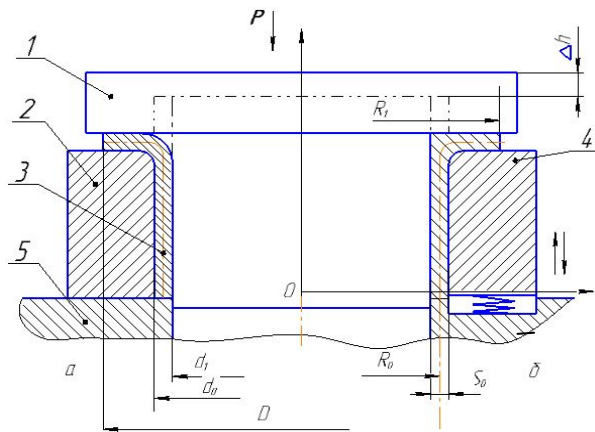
Схема раздачи и осадки трубной заготовки:
